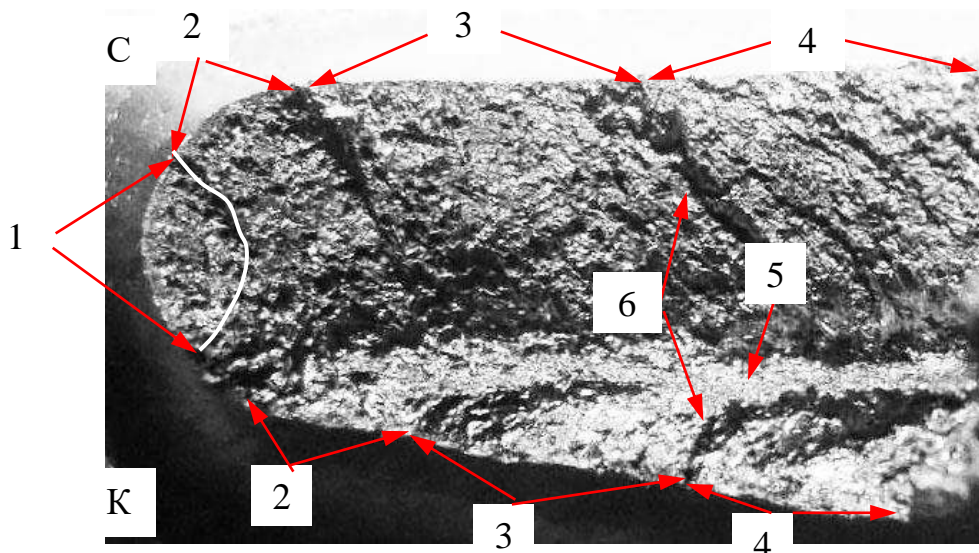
4 Макроизображение излома лопатки №10. Стрелками показаны: К – излом поверхностной трещины со стороны корытца, С – излом поверхностной трещины со стороны спинки, 1 – площадка отрыва, 2 - 4 – поверхностные трещины, 5 – полоса сброса, 6 – ступеньки.
